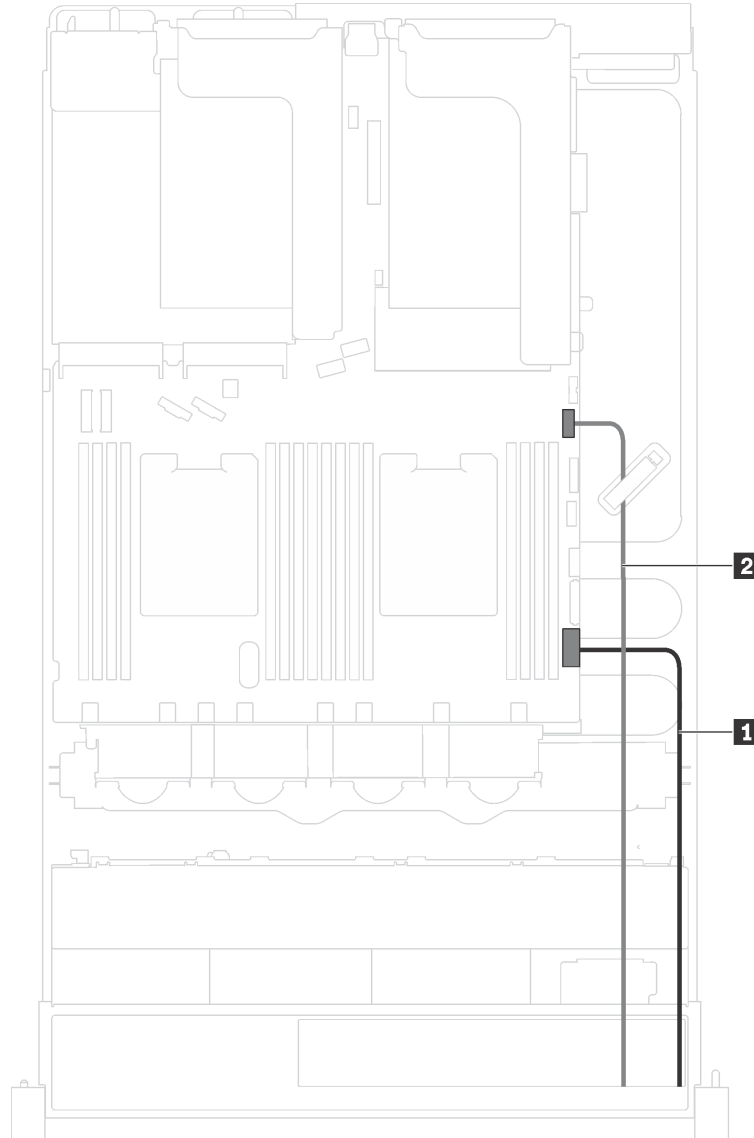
Disposición de los cables del conjunto de E/S frontal en el chasis
